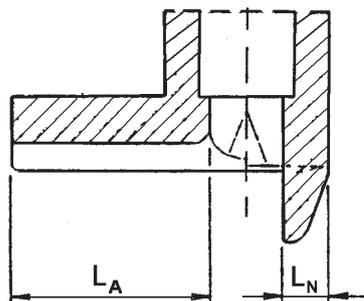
Mindestmaße an Schweißschuhen
